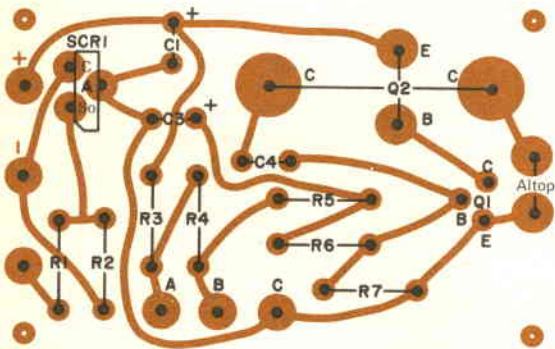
Disposizione dei componenti sul circuito stampato. Si noti come K1 e C2 non vengano montati sul circuito stampato stesso.
